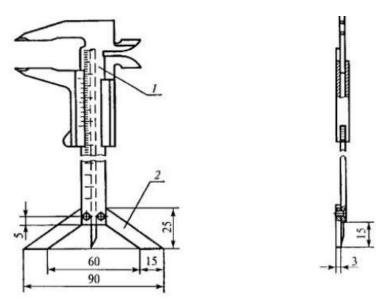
Штангенциркуль типа ШЦ- 1 с опорой 1 - штангенциркуль; 2 — опора
